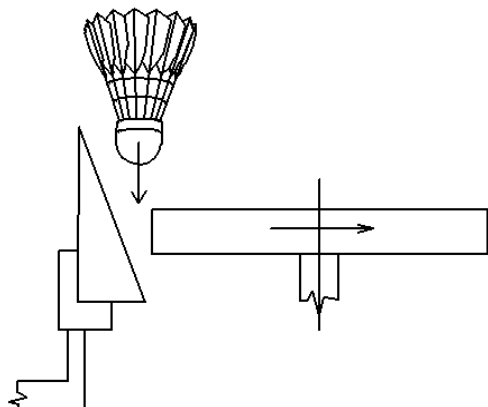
Rozevřací mechanismus podávacích kleští [5]
